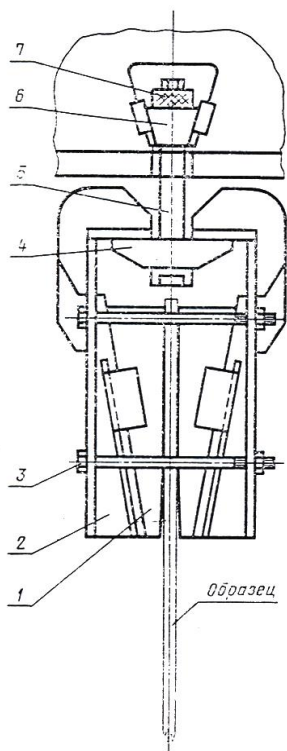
Пристосування для передачі розтягувального зусилля на зразок
